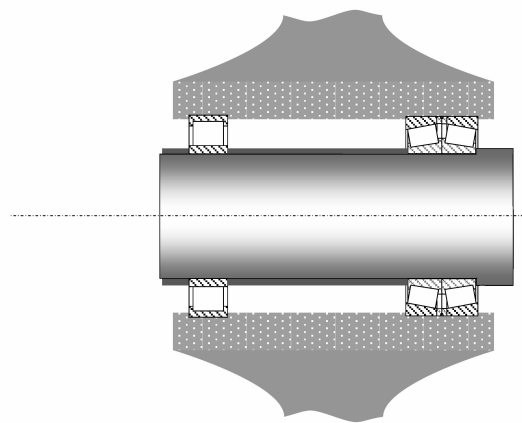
双列圆锥滚子轴承+圆柱滚子轴承
